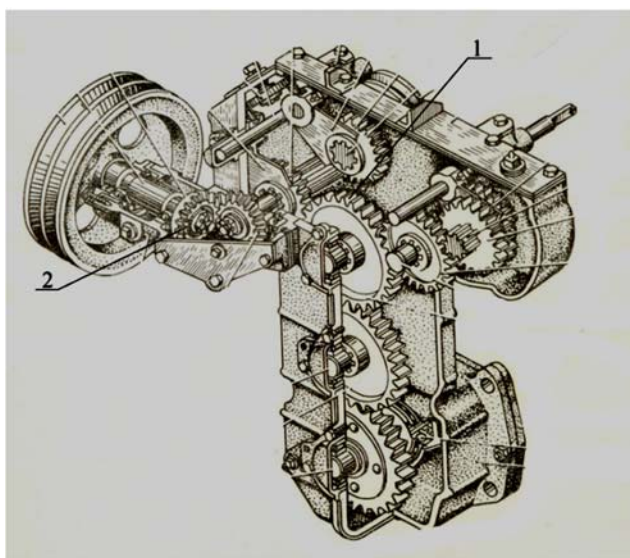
Общий вид раздаточного редуктора, применяемого для привода рабочих органов полунавесной хлопкоуборочной машины марки МХ-1,8
